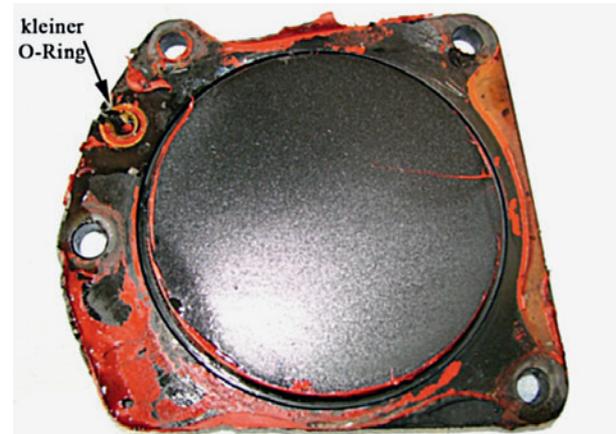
Kompressorblindflanschdeckel nach Demontage mit schadensursächlichem O-Ring und roter Dichtungsmasse
